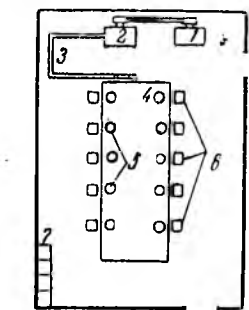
Схема расположения оборудования стеклодувной мастерской: 1 — мотор; 2 — воздуходувка; 3 — трубы от воздуходувки к рабочему столу; 4 — рабочий стол; 5 — стеклоплавильные лампы; 6 — табуреты; 7 — ящик для хранения дрота
